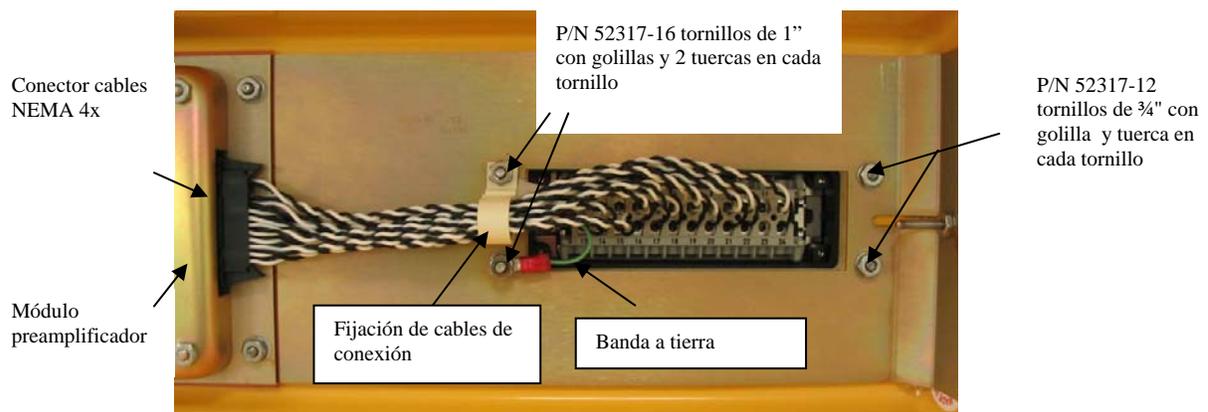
Ensamble de Soporte de Conector (Vista Interior de la Cubierta)
